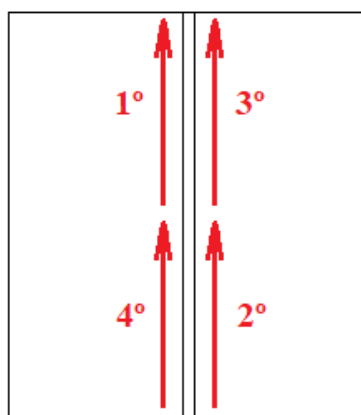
Sequência de cordões de soldadura no P.9 (Fonte: West-sea)
